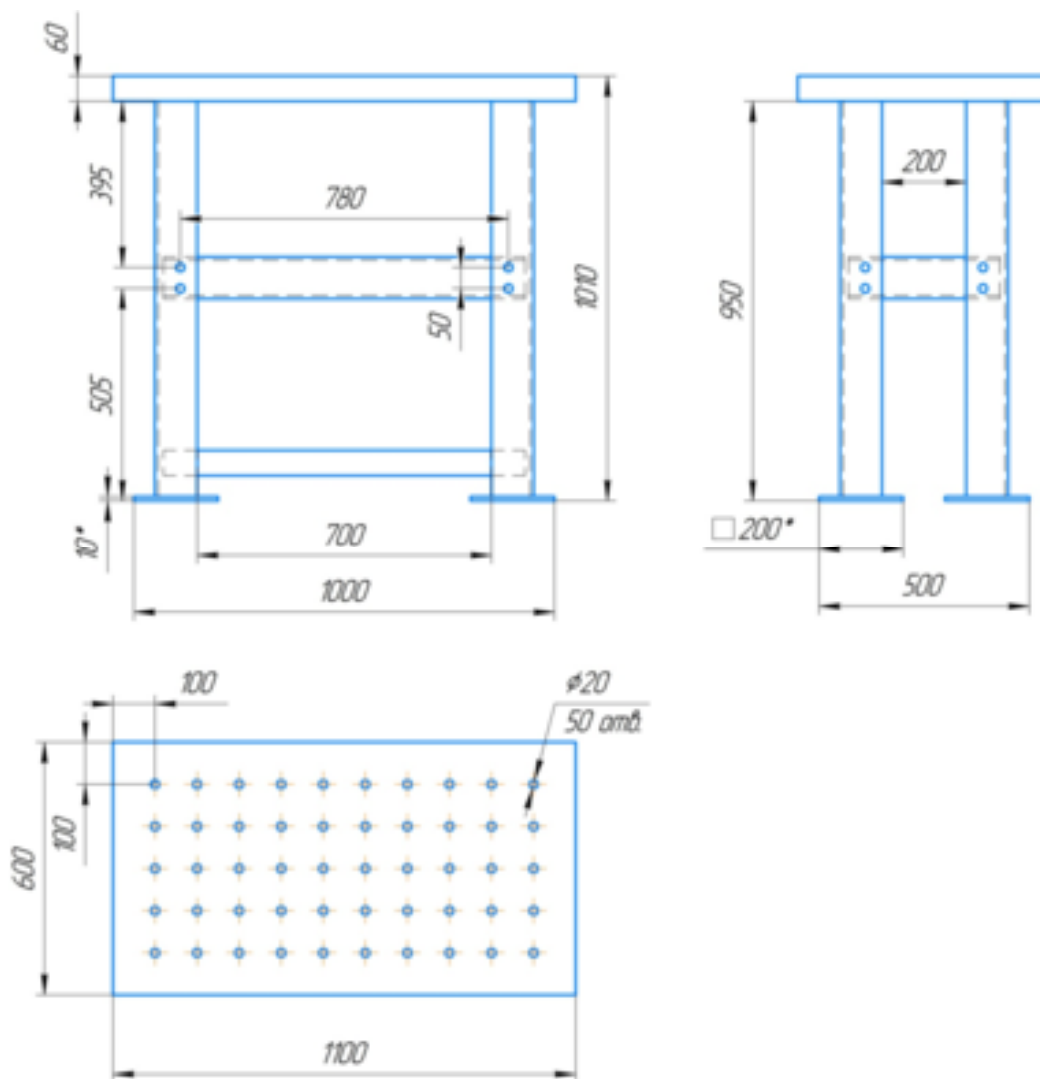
Общий вид сборочно-сварочного стола
